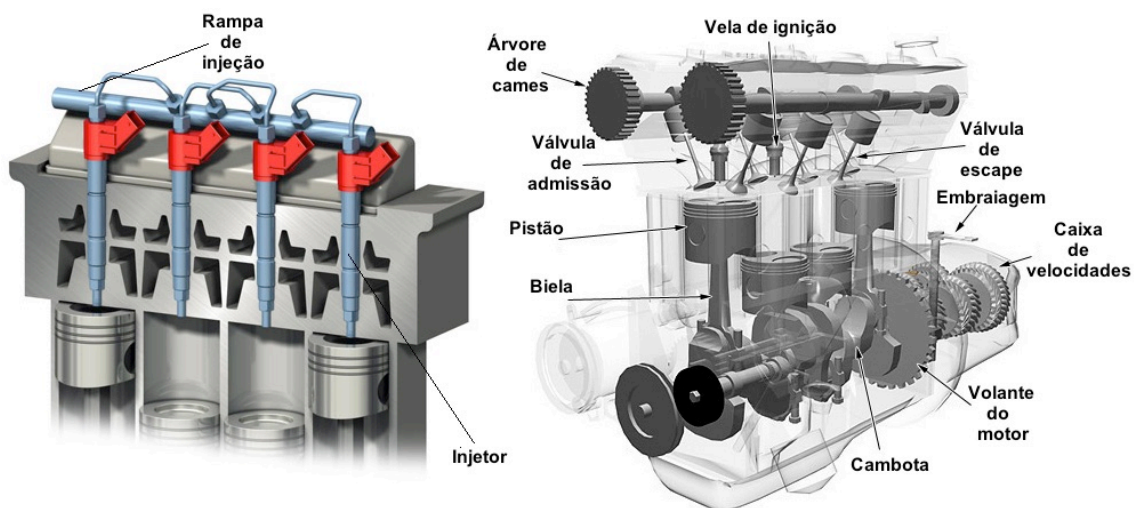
Principais componentes do motor a diesel (à esquerda) e a gasolina (à direita) [44].
